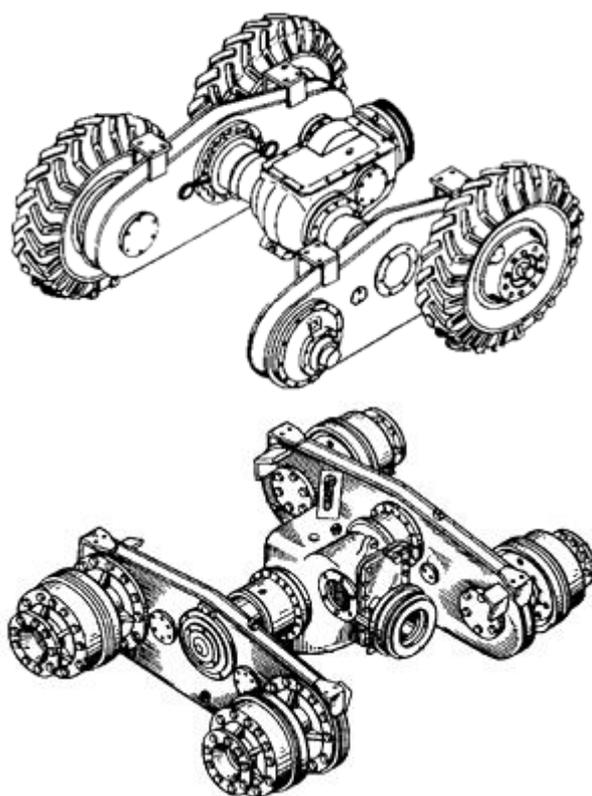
Задняя тележка ДЗ-122 форвардера ЛТ-189 (вид справа, вид слева)
